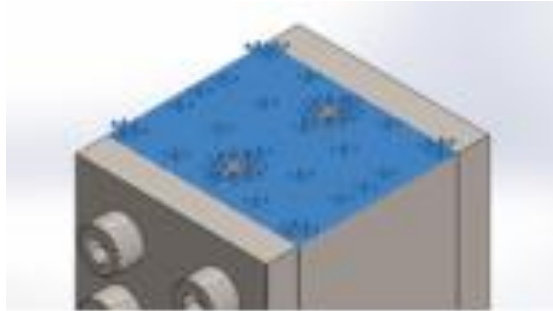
Zona de fixação do conjunto componente e acessórios.
